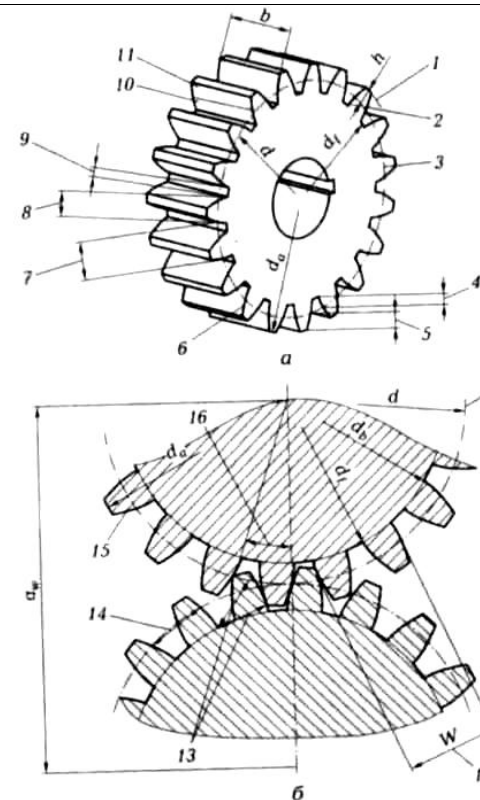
Параметры зубчатого колеса (а) и зубчатой передачи [б] .
